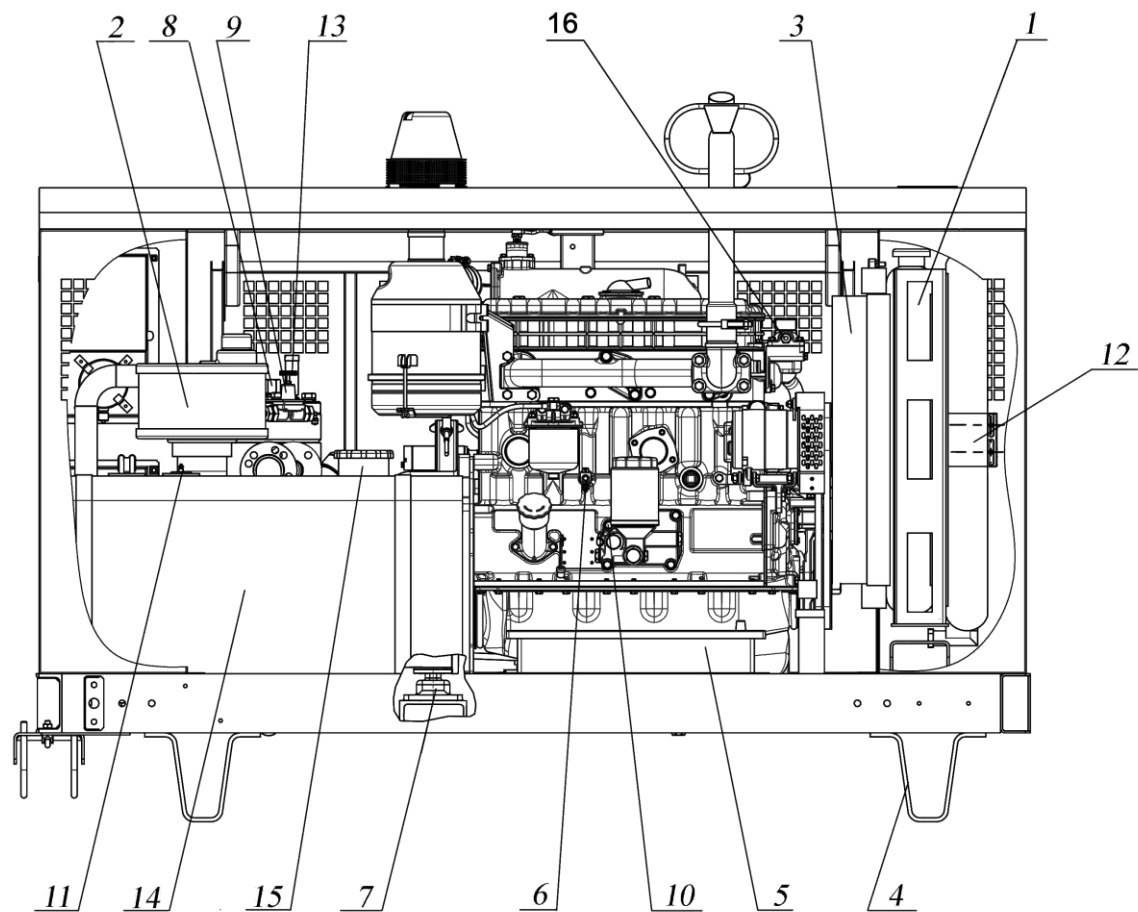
Габаритный чертеж компрессорной станции ЗИФ-ПВ-6/1,6 (АРМ9-21.1-123).
